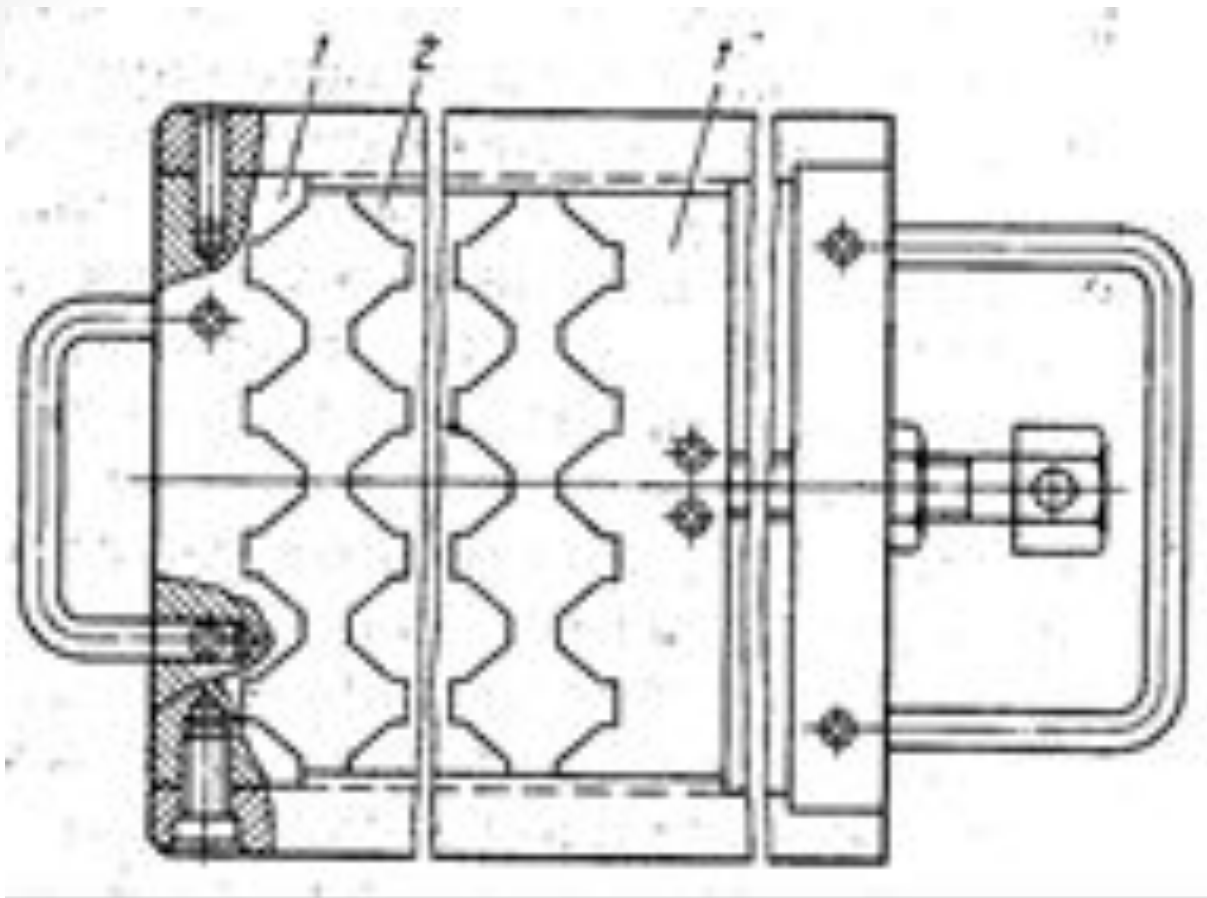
Многоместное приспособление для шлифовки торцов пальцев
